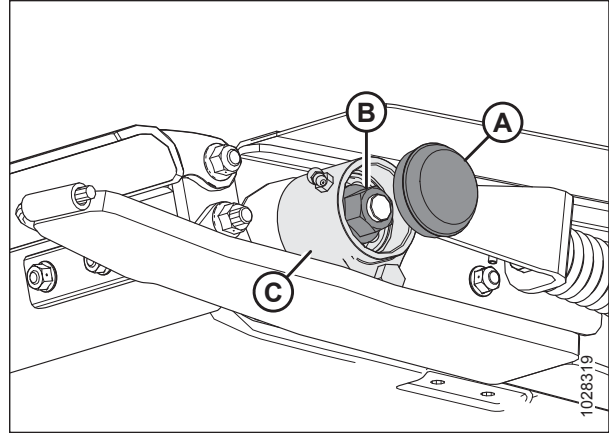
Carcasa del rodamiento del rodillo tensor
